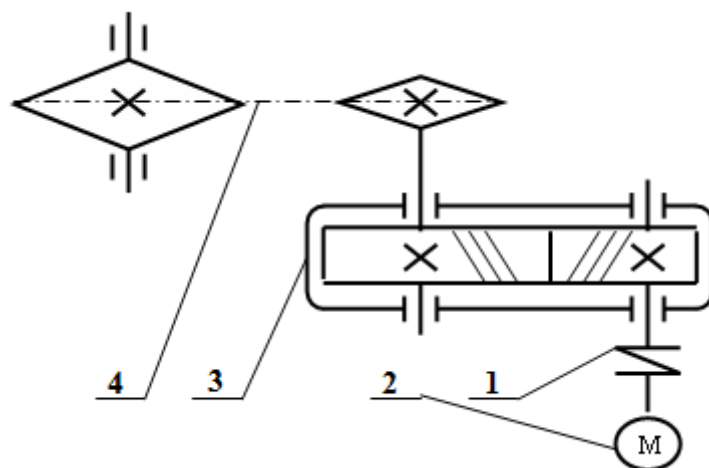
Привод стрічкового конвеєра: 1 – муфта типу МПВП, 2 – електричний двигун, 3 – одноступінчатий циліндричний косозубий редуктор, 4 – ланцюгова передача.
